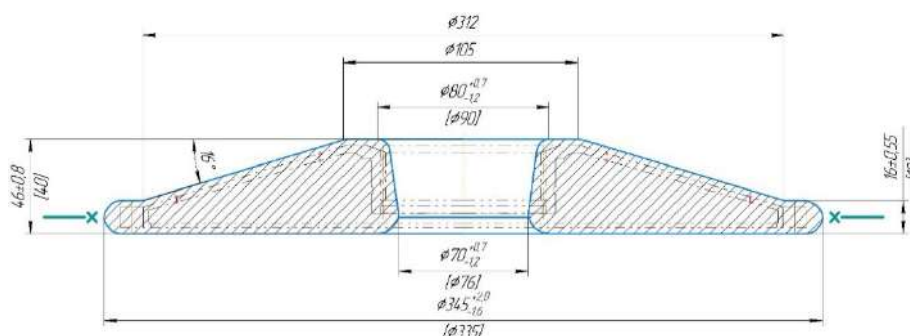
Ескіз заготовки, штампованої на КГШП
